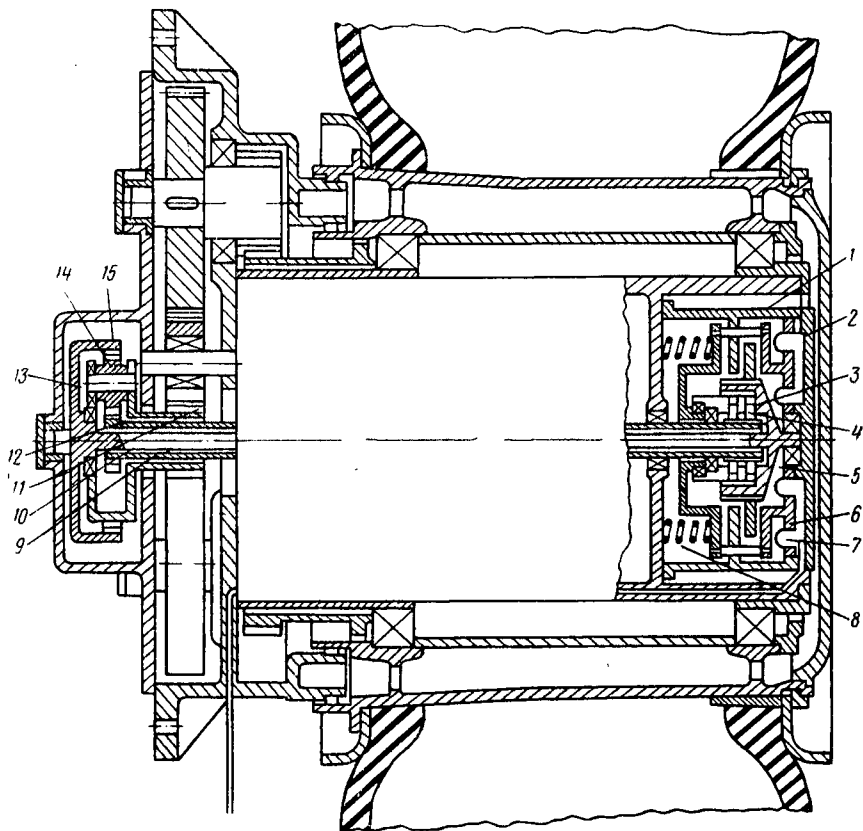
Мотор-колесо с двухскоростным редуктором:
